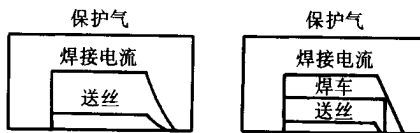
熔化极气体保护焊焊接程序
